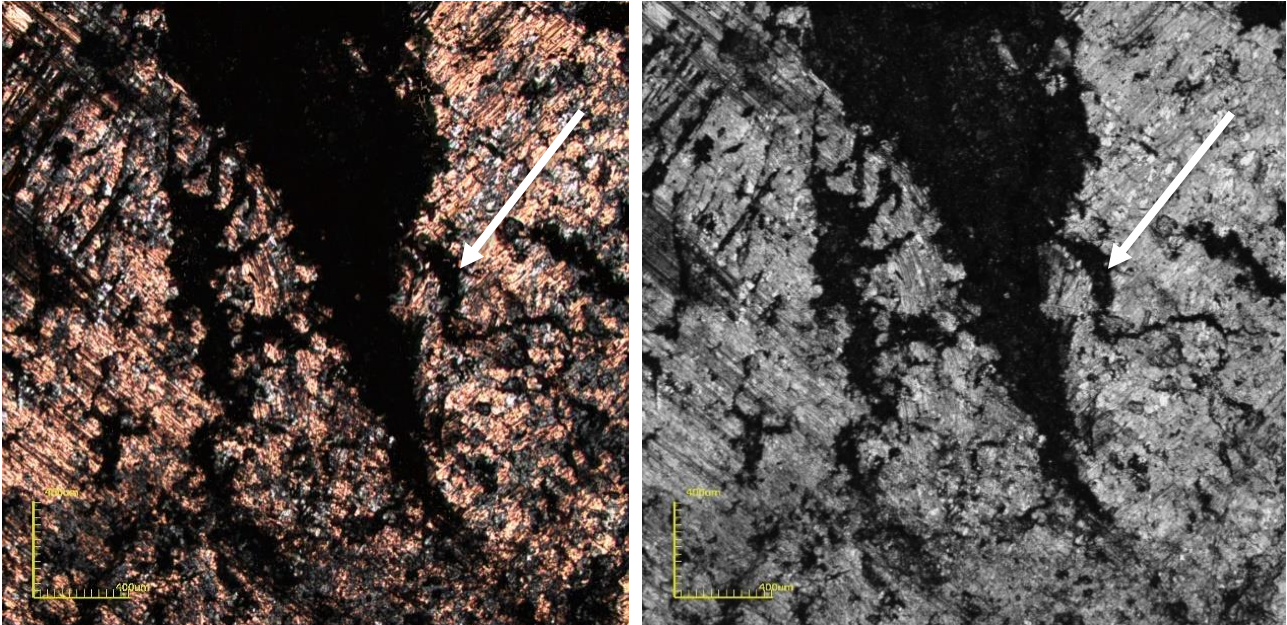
Fratura gerada durante o ensaio de compressão.
